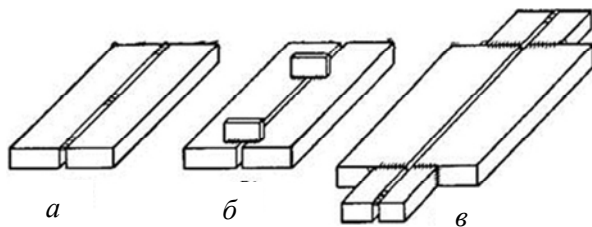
Способы закрепления деталей перед сваркой:
